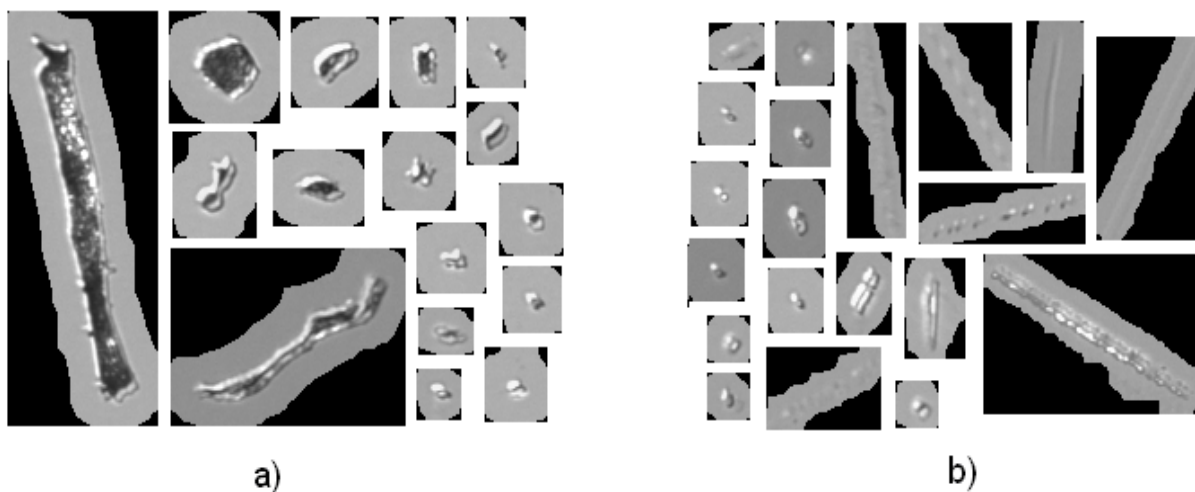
Exemples de défauts à classer : a) défaut de type « poussière » ; b) autre type de défauts .
